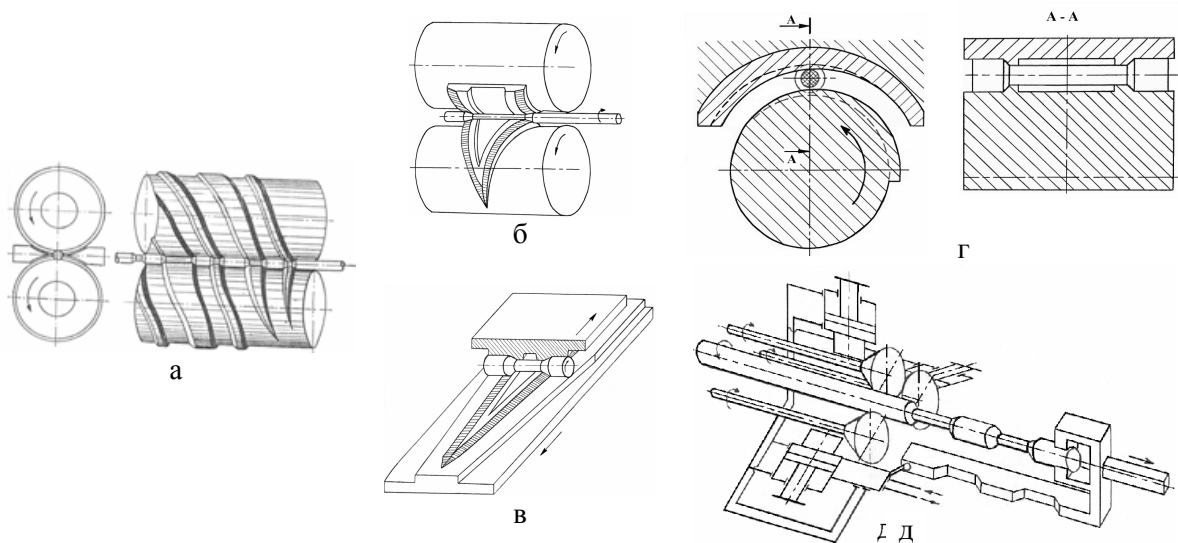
Способы получения профилированных заготовок поперечной прокаткой (по С.Н. Добровлянскому [22]): а) поперечно-винтовая прокатка; б) поперечно-клиноватая прокатка в валках; в) поперечно-клиноватая прокатка в досках (плитах); г) валкосегментная прокатка; д) прокатка в трехвалковых станах конструкции ВНИИМетМаша
